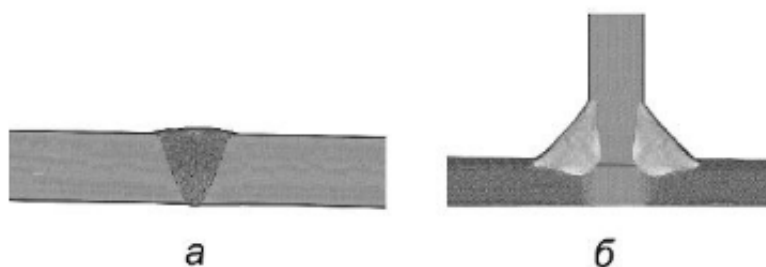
Типы сварных швов: а – стыковой шов; б- угловые швы
